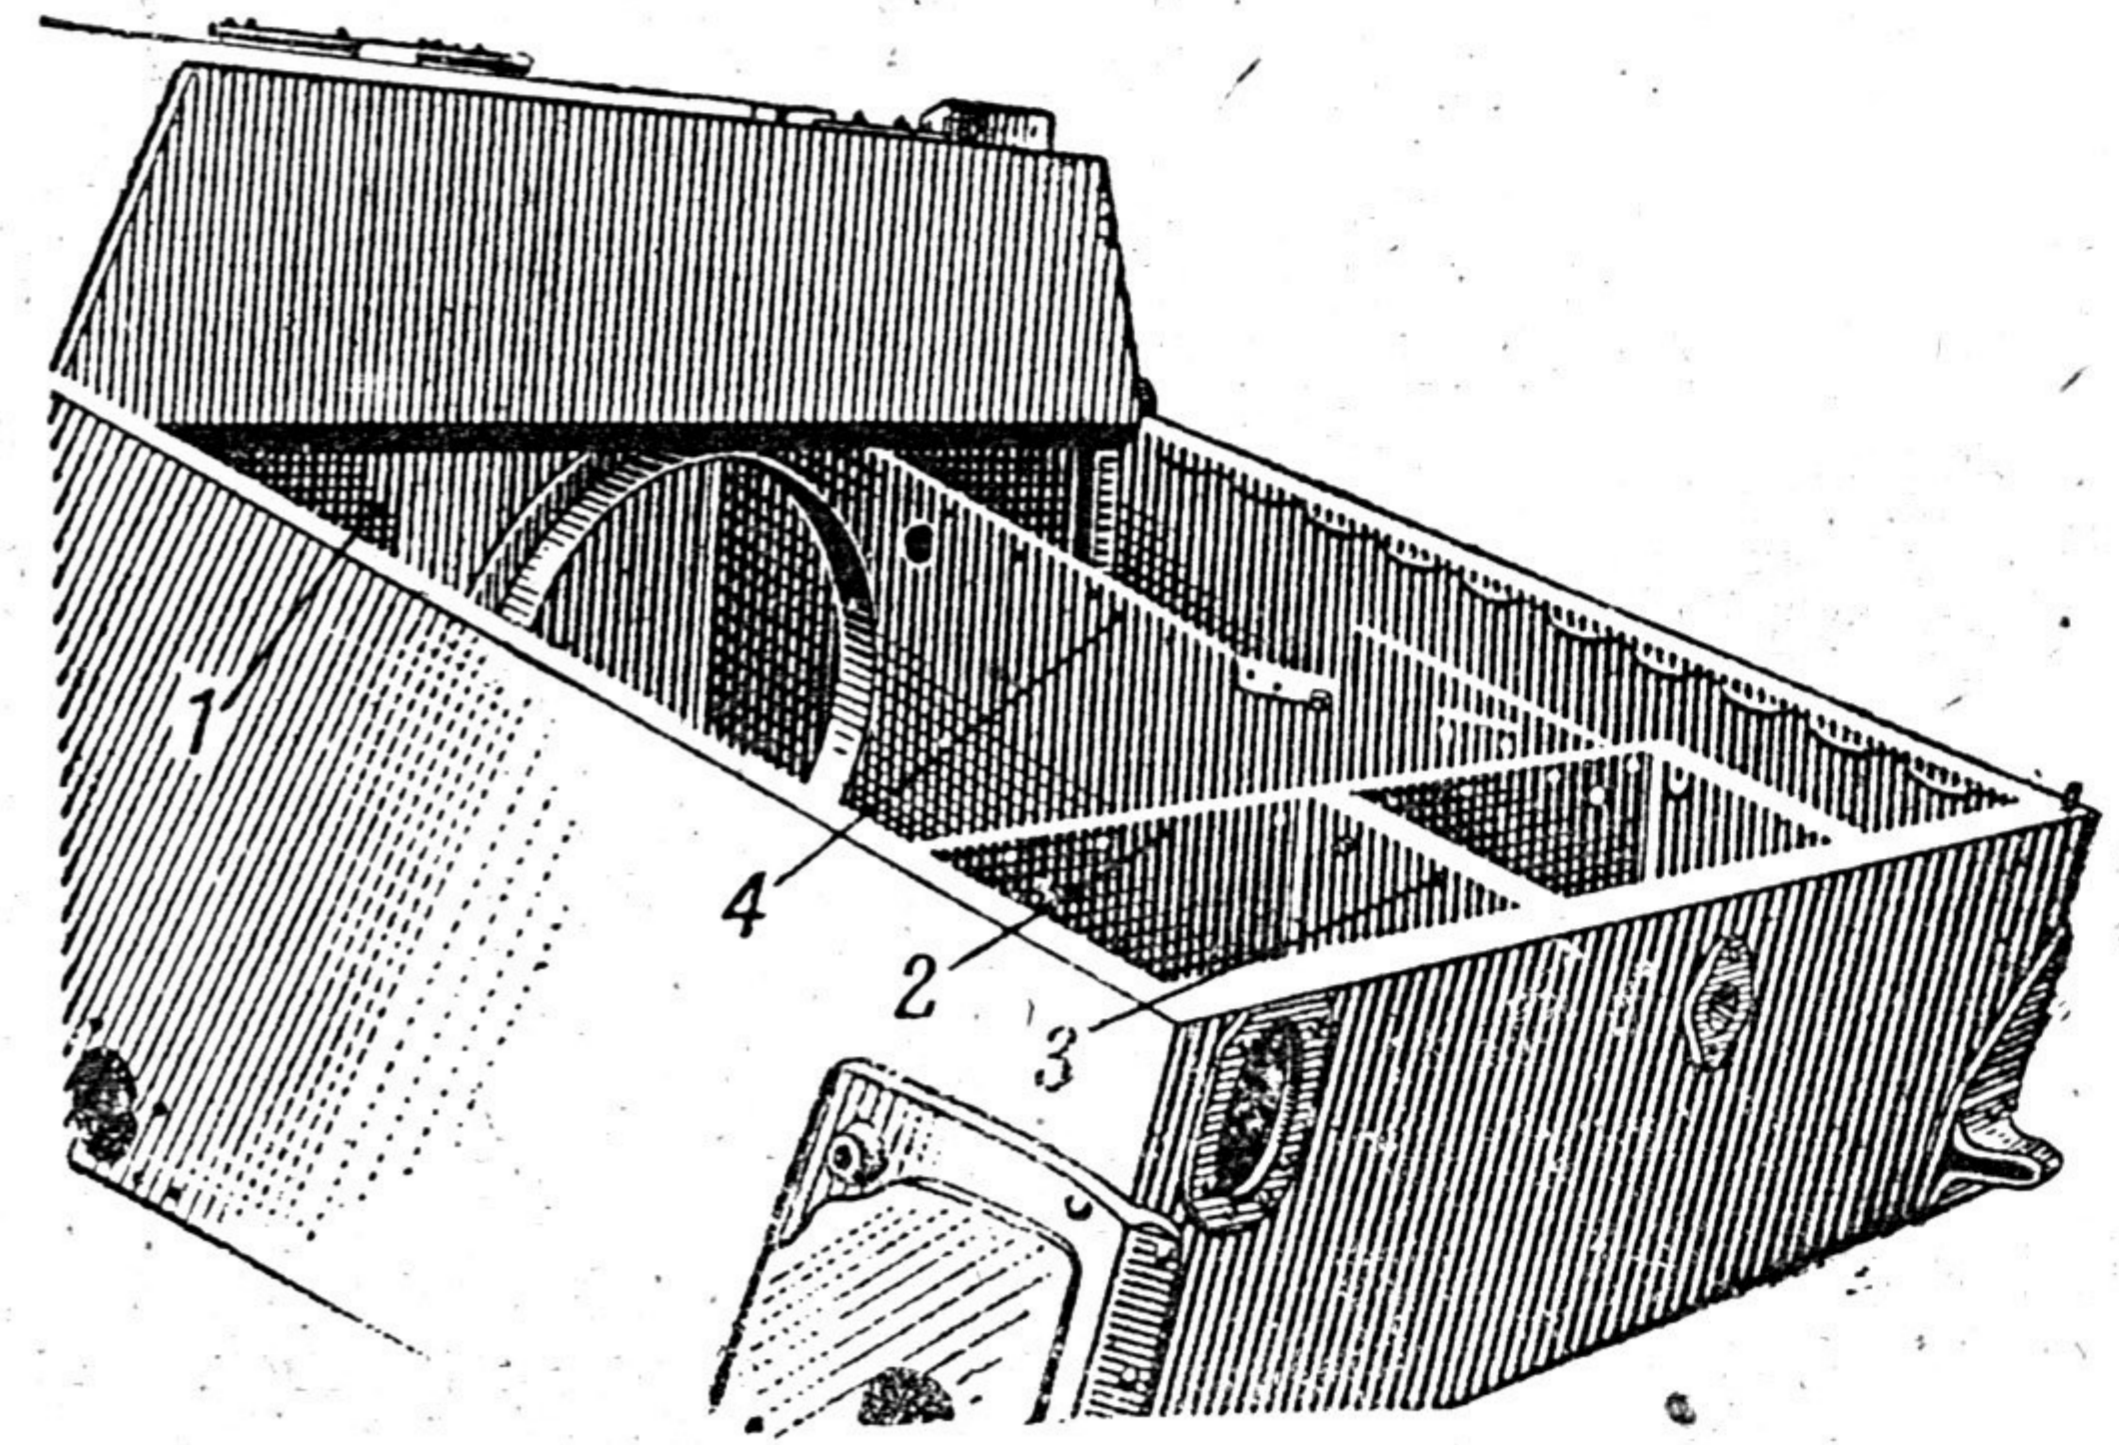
Расположение перегородок в корпусе с прямой подбашенной коробкой (общий вид):
